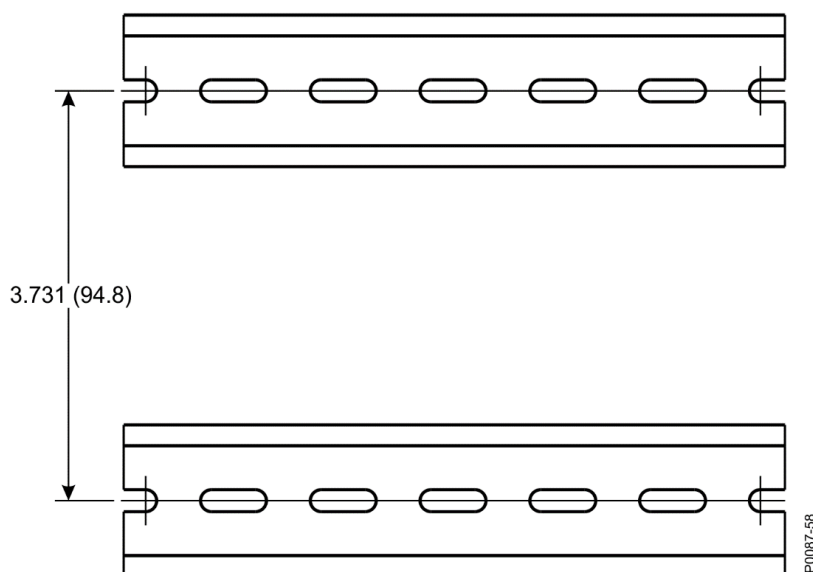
DIN 导轨安装尺寸，型号 xRxxxxxxx
